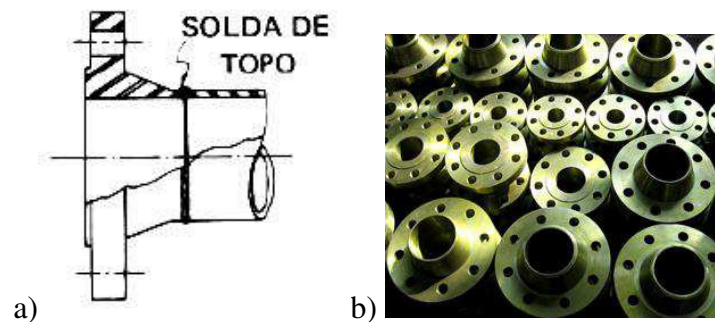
a) Desenho Representativo de um Flange de Pescoço (SENAI, 1997) b) Flanges de Pescoço (AHAD Tubeline co., 2012)
